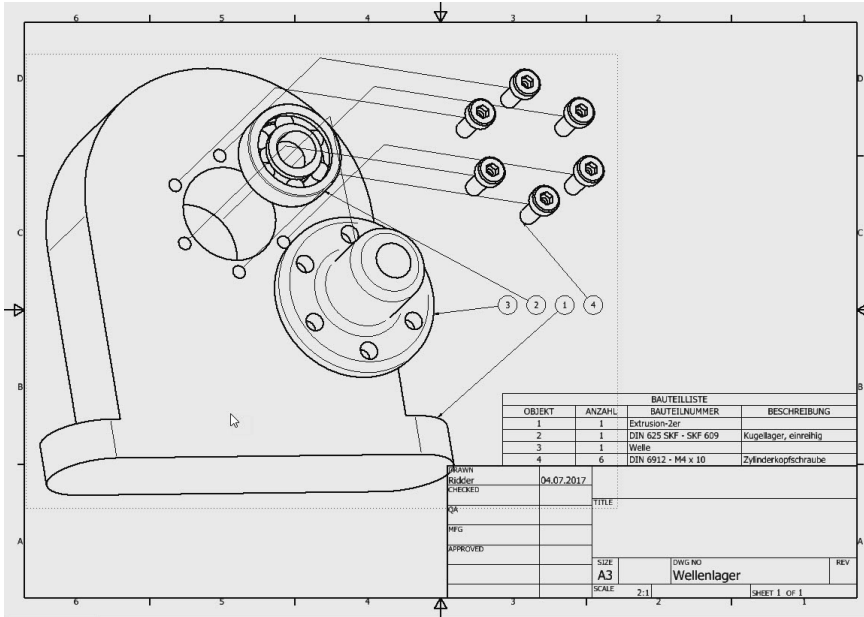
Zeichnung der Explosionsansicht mit Positionsnummern und Stückliste
